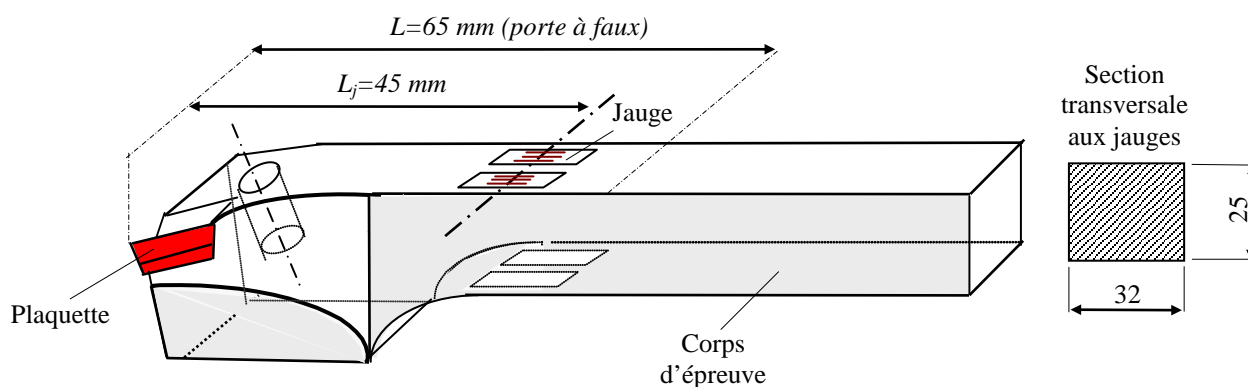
Dimensions du corps d'épreuve conçu.
